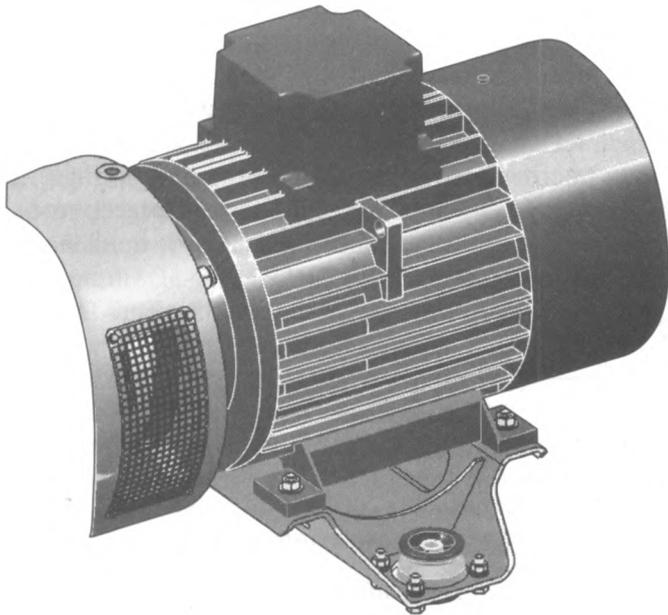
Асинхронный двигатель привода безмасляного двухступенчатого компрессора Bujan 20
